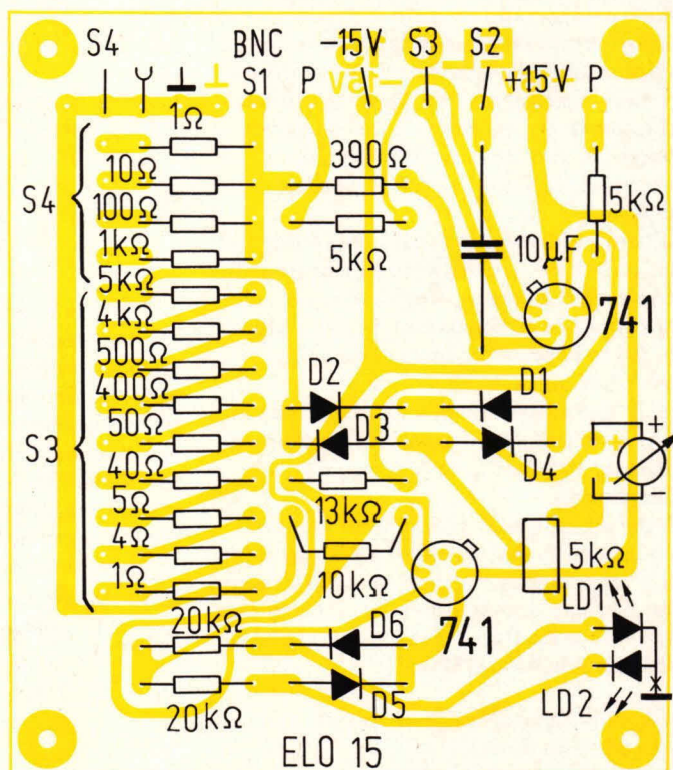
Print van de millivoltmeter (soldeerzijde) en montageschema (rechts).
